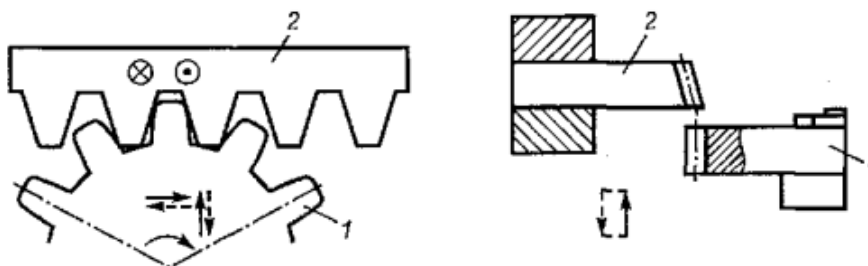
Обробка великомодульних коліс зубчатыми гребінками:
